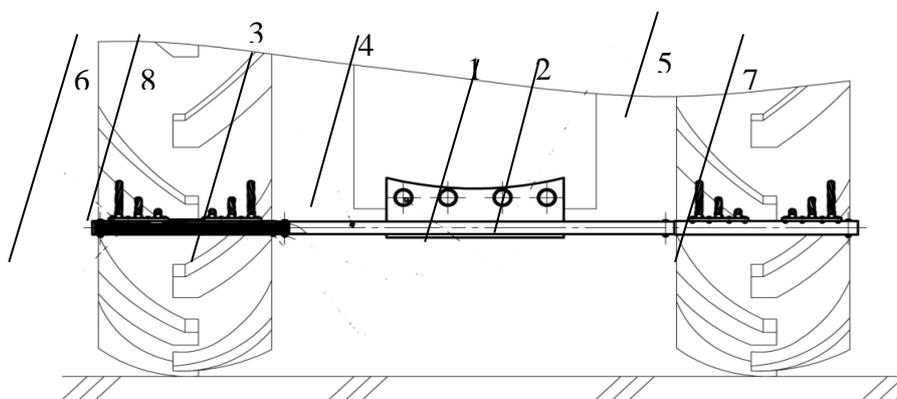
Устройство для очистки рисунка протектора колёсного движителя универсально-пропашного трактора в движении (1-несущая ось, 2-торсионные соосные цельнометаллические стержни, 3- упругая муфта, 4- кронштейн, 5- трактор, 6- опорно-скребковый механизм, 7-опорная площадка, 8- скребок)
